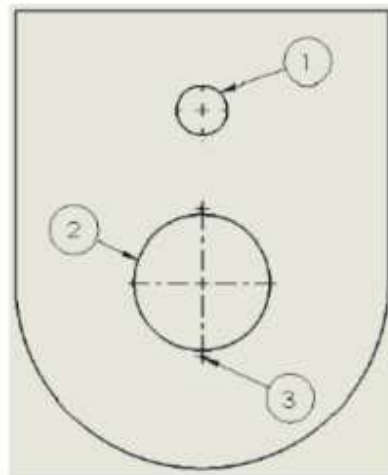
Placa soporte del embudo (CAD). Fuente: Autor
